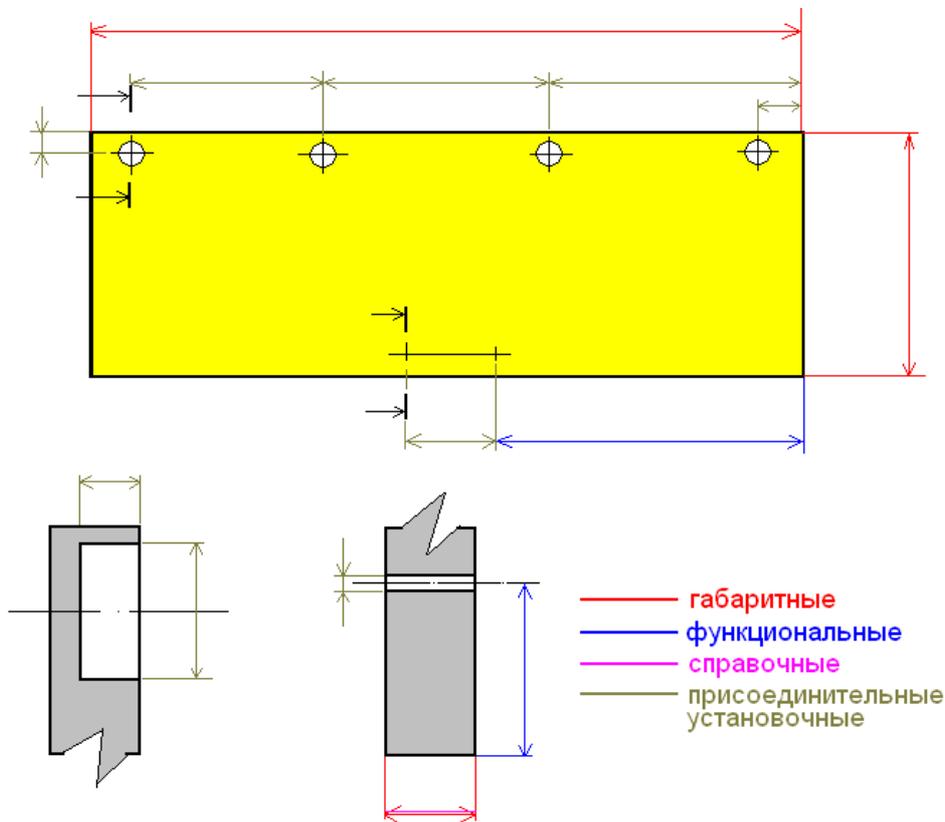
Чертеж дверки. Виды размеров в конструкциях мебели
